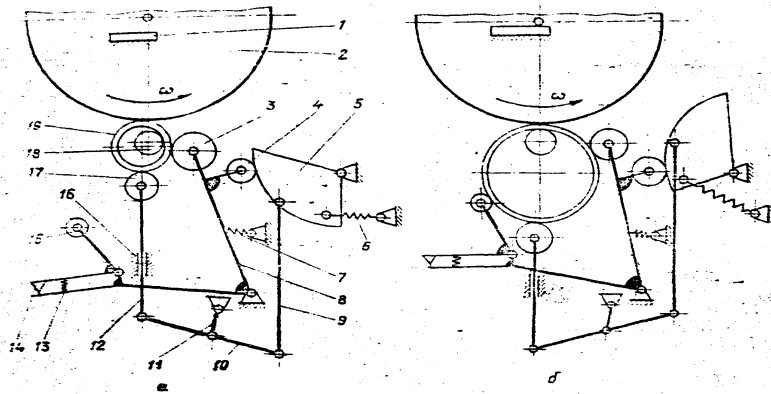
Схема розкочування кілець шарикопідшипників на автоматі мод. 4К-0-46:
